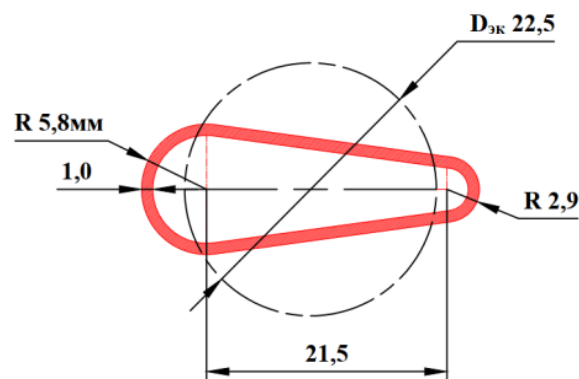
Поперечное сечение каплевидной трубы без нагрузки
